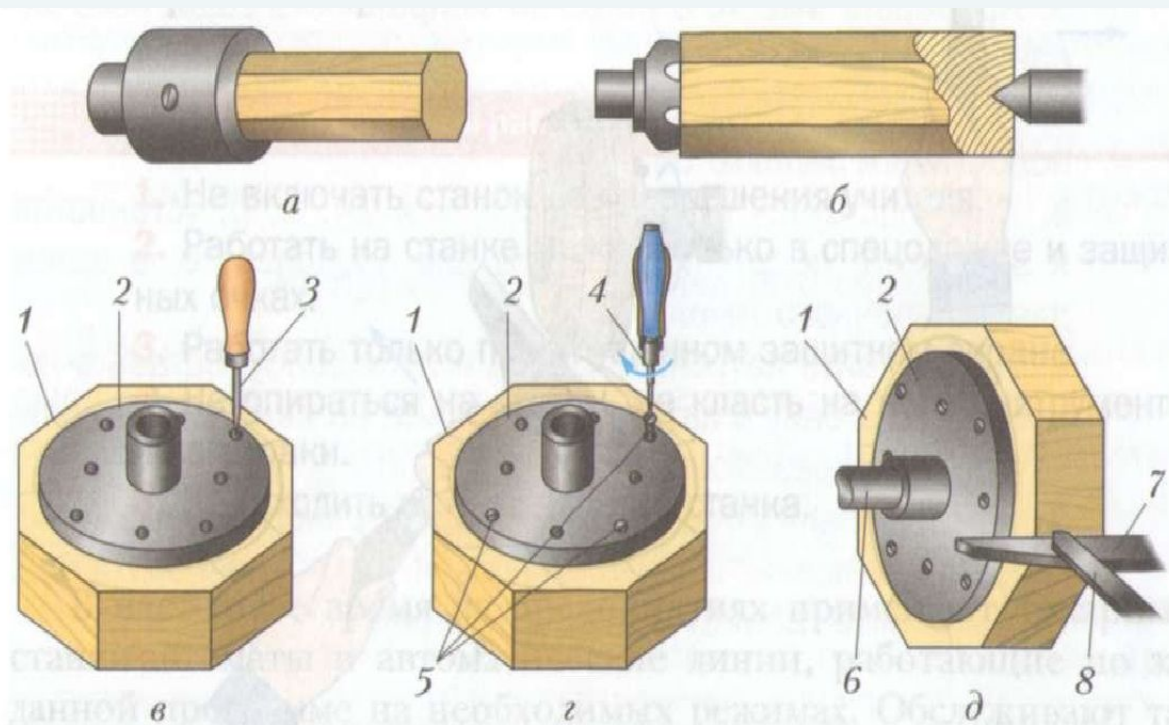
Крепление заготовки: *а* – в патроне винтом; *б* – с помощью трезубца и заднего центра; *в, г, д* – на планшайбе: 1 – заготовка; 2 – планшайба; 3 – шило; 4 – отвёртка; 5 – шурупы; 6 – шпиндель; 7 – подручник; 8 – режущий инструмент (стамеска)
